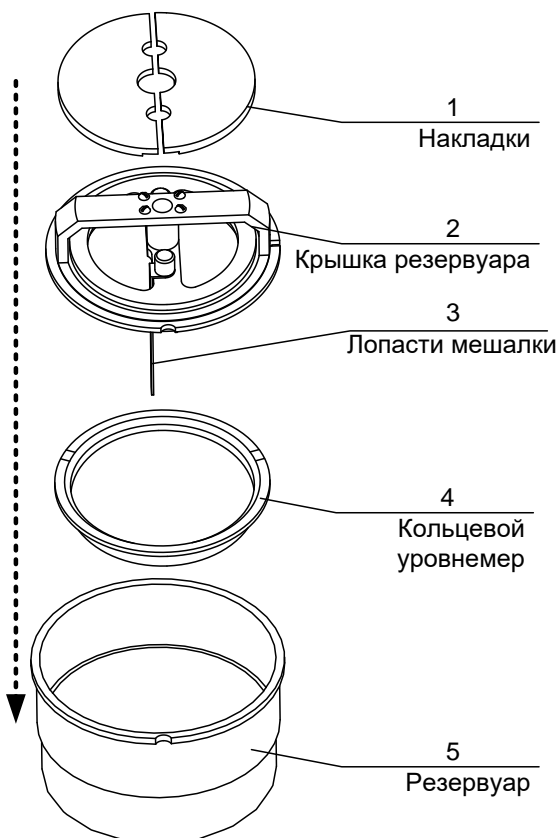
Порядок сборки узла резервуара с мешалкой
